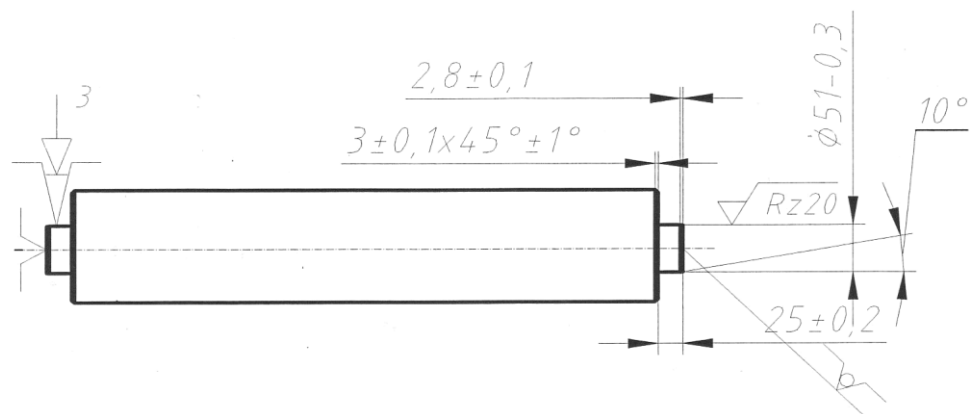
Ескіз обробки деталі операція №020
